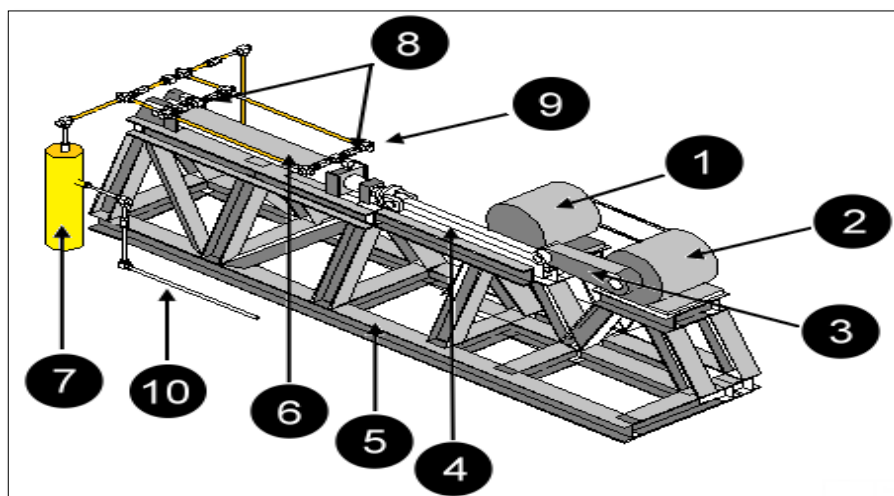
Compresor para Unidad de Bombeo Mecánico.
